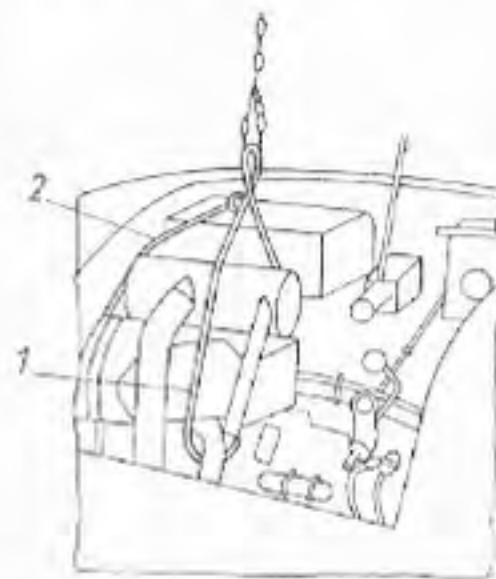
Přední levé pružné lůžko poháněcí soustavy
